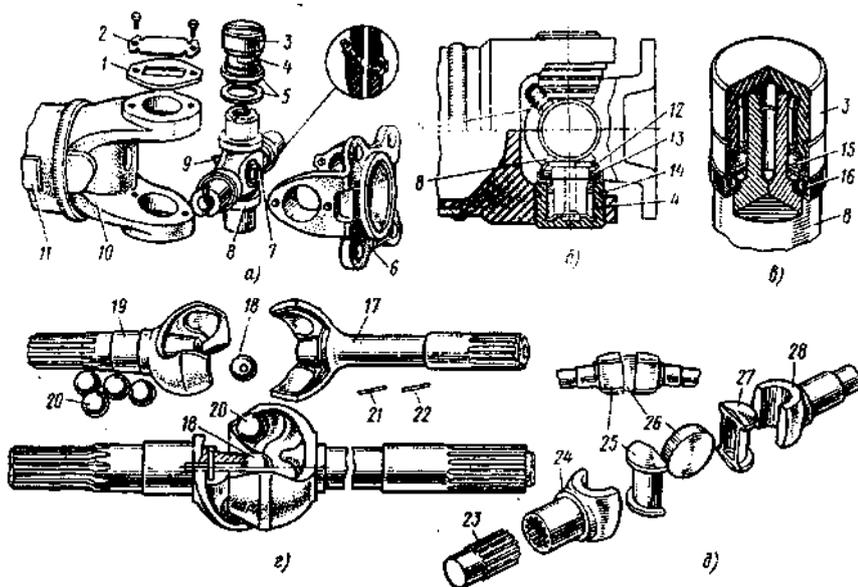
Карданные шарниры: *а* — *в* — неравных угловых скоростей; *г* и *д* — равных угловых скоростей; 1—крышка; 2—стопорная пластина; 3—стакан подшипника; 4 — иголки; 5— войлочные манжеты; 6, 10, 24 и 28 — вилки, 7 — предохранительный клапан; 8— крестовина; 9 —масленка; 11--карданный вал; 12—отражатель; 13— самоподжимная манжета, 14— стопорное кольцо; 15 и 16— манжеты радиального и торцового уплотнений, 17 — внутренний кулак; 18 —центральный шарик, 19— наружный кулак; 20— ведущие шарики; 21 — штифт; 22—шпилька; 23 — полуось; 25 и 27— полуцилиндрические кулаки; 26 — центральный диск.
